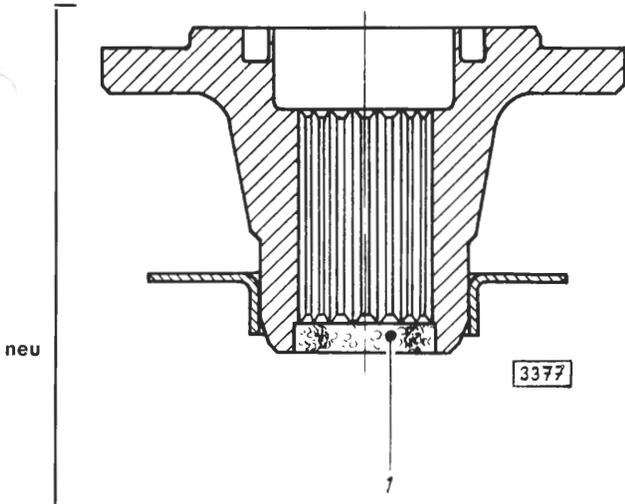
Antriebkegelradflansch vor dem Aufstecken mit Dichtungsmasse versehen
